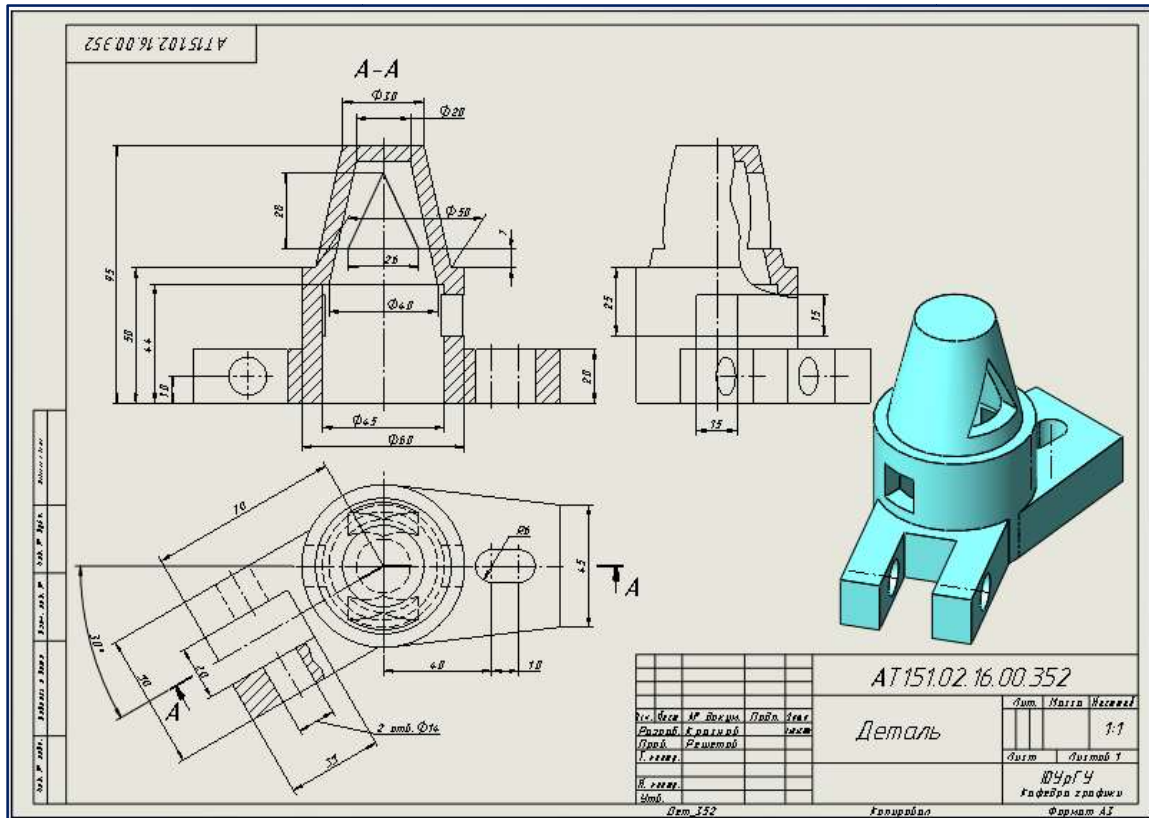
Чертёж детали, содержащий ломаный разрез
